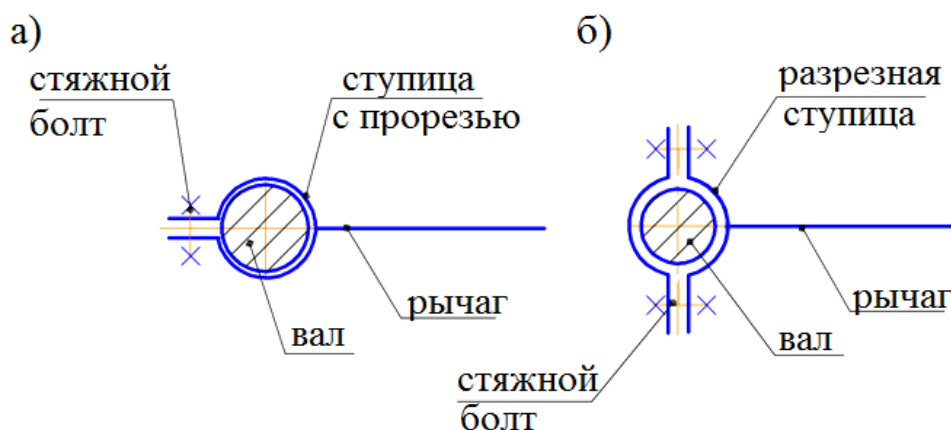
Схемы клеммового соединения: а – ступица с прорезью; б - с разъёмной ступицей.
